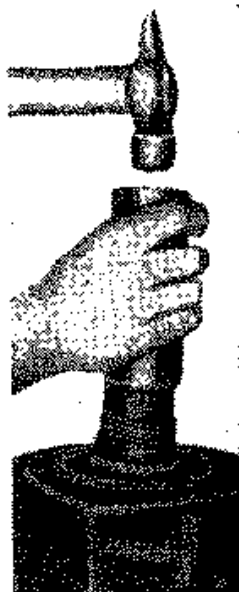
Напрессовка заднего подшипника на вторичный вал
